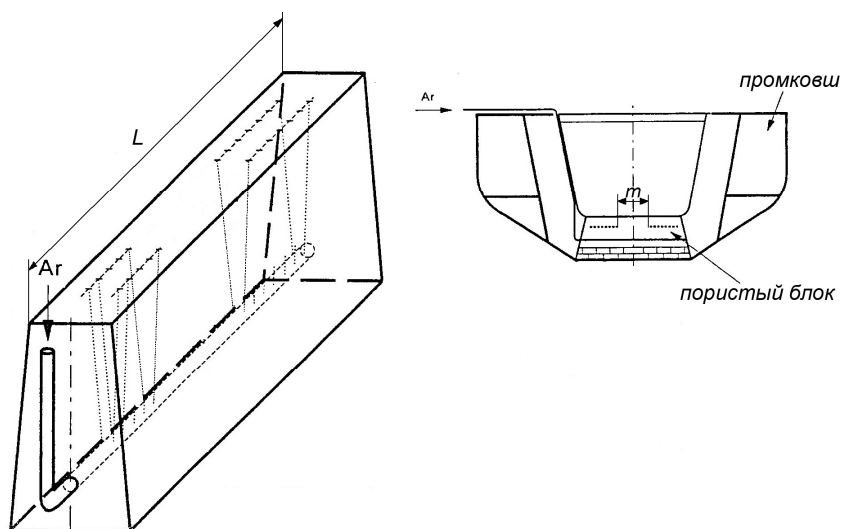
Конструкция продувочного блока промежуточного ковша
